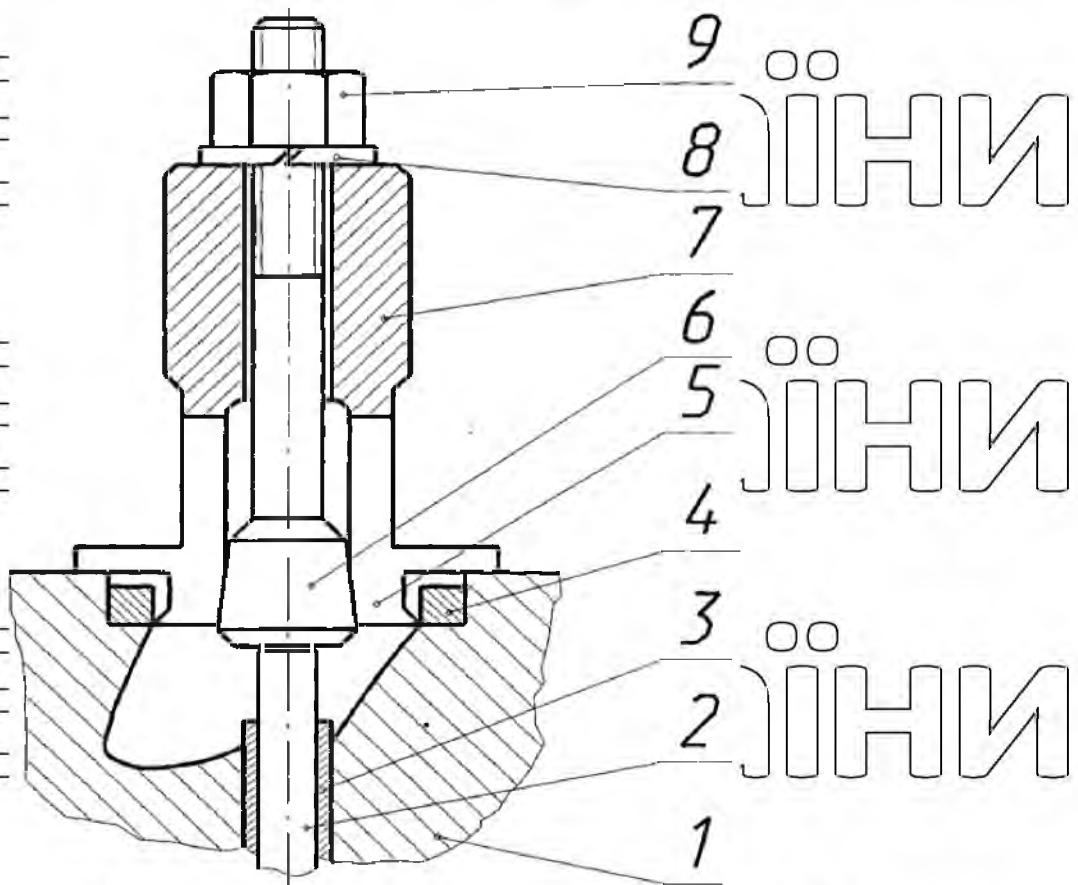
Пристрій для пресування сідла клапанів з ГБИ: 1 - головка блоку; 2 - стрижень; 3 - направмна втулка; 4 - сідло клапана; 5 - цангова ручка; 6 - конус; 7 - корпус екстрактора; 8 - шайба; 9 - гайка.
